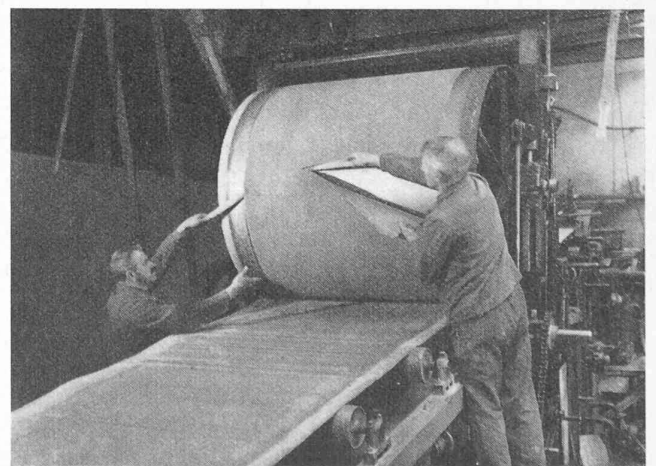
Machine à carton. La plaque est coupée sur le cylindre à format.
